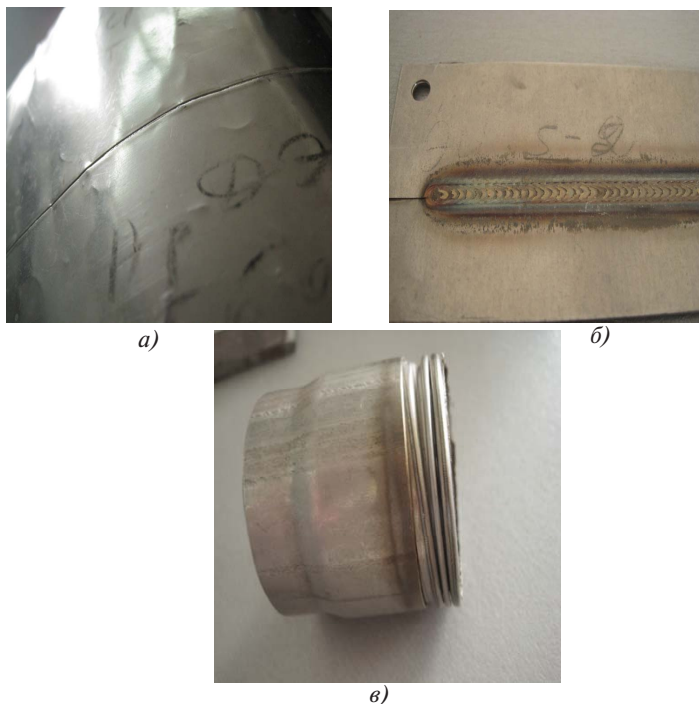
Сварные узлы, изготовленные из тонколистовой нержавеющей стали: *а)* сварка кольцевого стыка обечайки; *б)* импульсная ПРДС; *в)* сильфонный компенсатор
